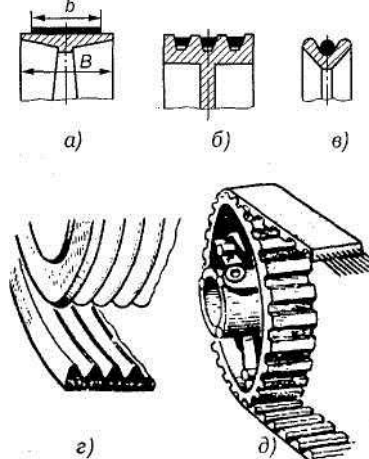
Типы ремней ременных передач: *а* — плоский ремень; *б* — клиновый ремень; *в* — круглый ремень; *г* — поликлиновый ремень; *д* — зубчатый ремень
